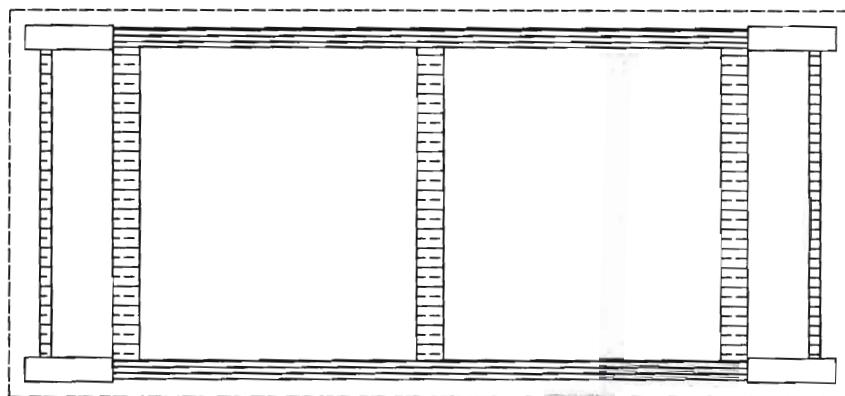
DETAIL DE LA PLANCHE DE TRAVAIL OU TOP
